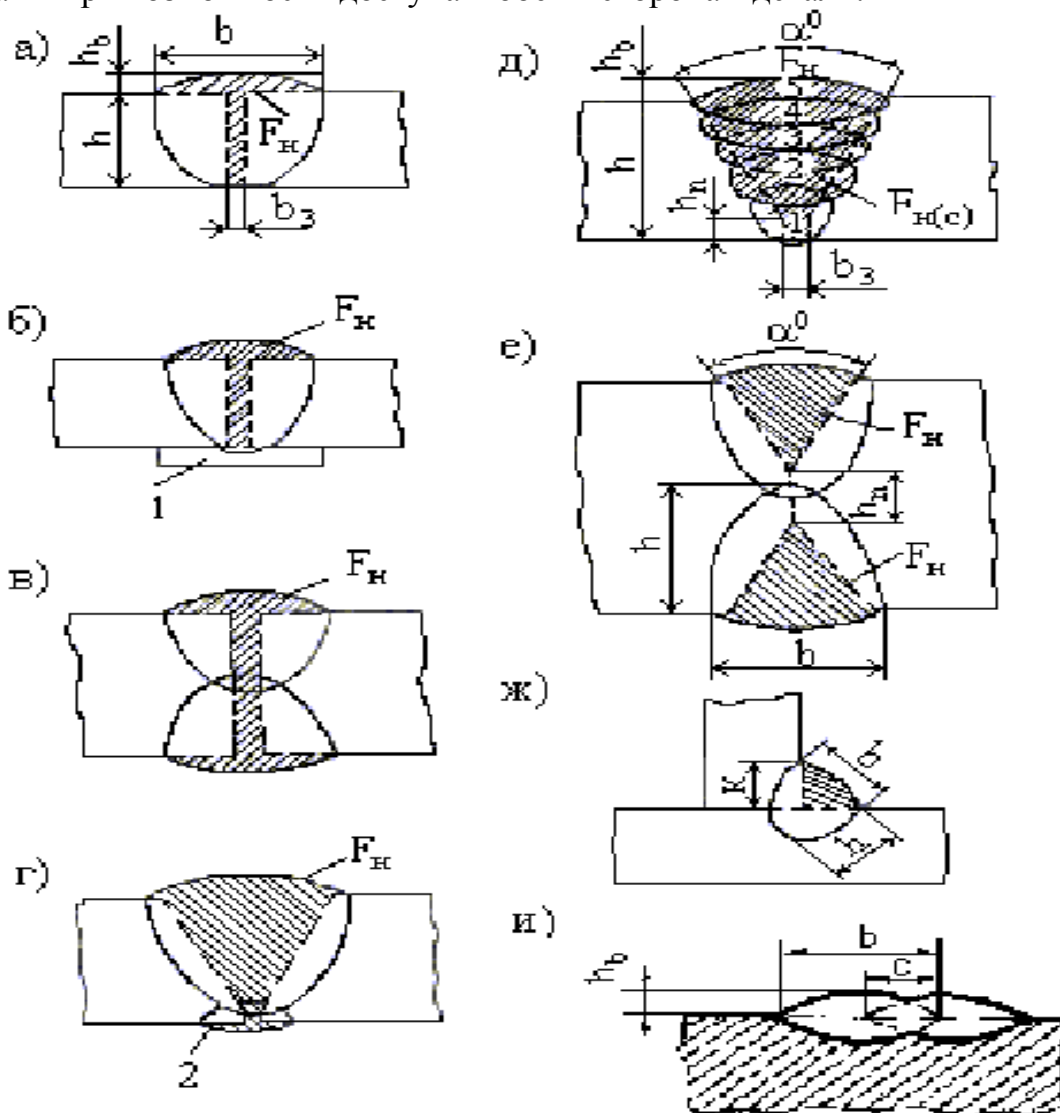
Размеры и форма разделки кромок и сварного шва:
